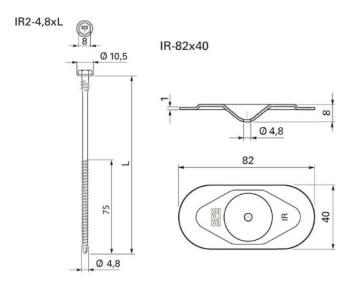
Vis SFS INTEC "IR2-4,8xL" fastener + plaquette de fixation "IR-82x40"
